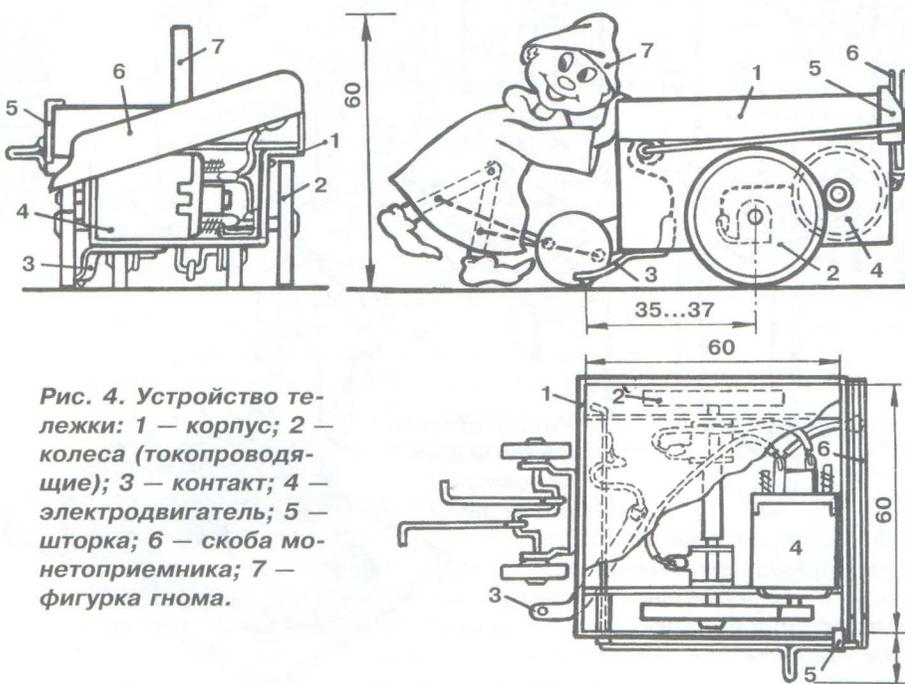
Устройство тележки: 1 — корпус; 2 — колеса (токопроводящие); 3 — контакт; 4 — электродвигатель; 5 — шторка; 6 — скоба монетоприемника; 7 — фигурка гнома.
